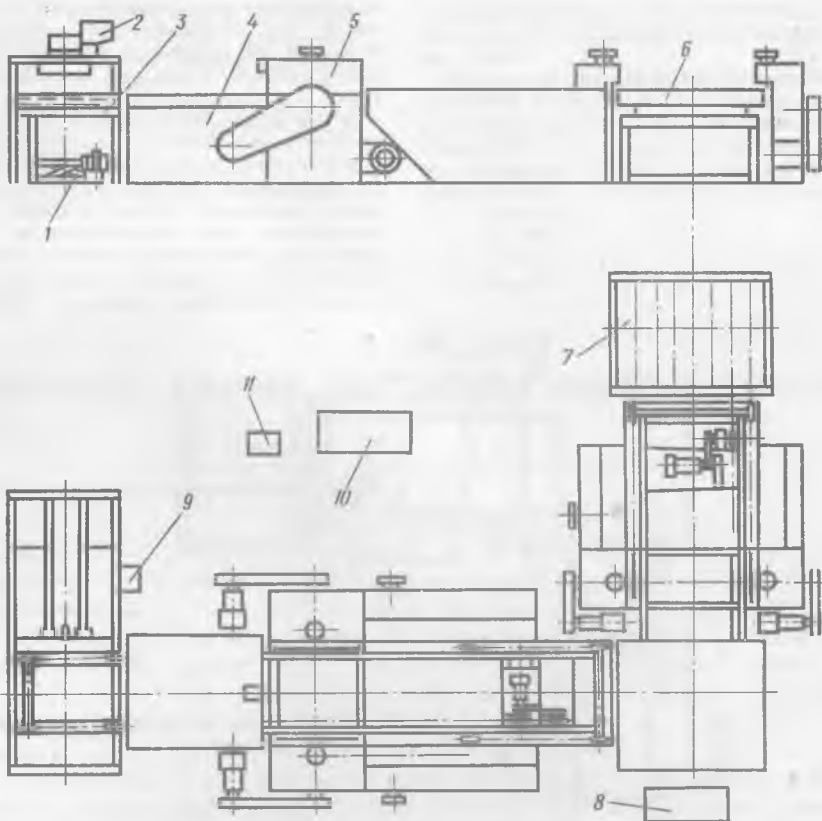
Станок для обрезки фанеры в пачках ФП-119
